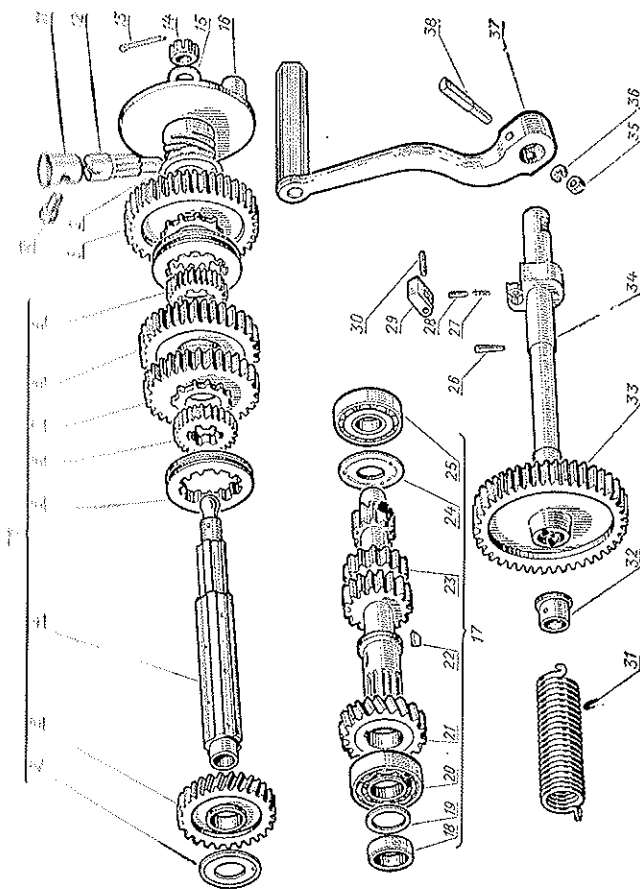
Вала и шестерни коробки перемены передач: 1 — вал вторичный в сборе; 2 — шайба вторичного вала; маслоотражательная шайба; 3 — шестерня IV передачи; 4 — вал вторичный; 5 — муфта включения; 6 — муфта вторичного вала шлицевая; 7 — шестерня III передачи; 8 — шестерня II передачи; 9 — шестерня I передачи; 10 — винт; 11 — втулка привода к спидометру; 12 — шестерня привода к спидометру; 13 — шплинт 3×30 гайки вторичного вала; 14 — гайка прорезная 14×1,5; 15 — шайба; 16 — диск муфты кардана; 17 — вал первичный в сборе; 18 — муфта первичного вала; 19 — прокладка переднего подшипника; 20 — подшипник № 205; 21 — шестерня IV передачи первичного вала; 22 — шпонка; 23 — вал первичный; 24 — шайба маслоотражательная; 25 — ролик коподшипник № 12204; 26 — штифт конический; 27 — пружина; 28 — штифт пружины; 29 — собачка; 30 — ось собачки; 31 — пружина; 32 — втулка; 33 — шестерня пускового механизма; 34 — вал; 35 — гайка М5×1; 36 — шайба; 37 — рычаг пускового механизма; 38 — клинок рычага пускового механизма.
